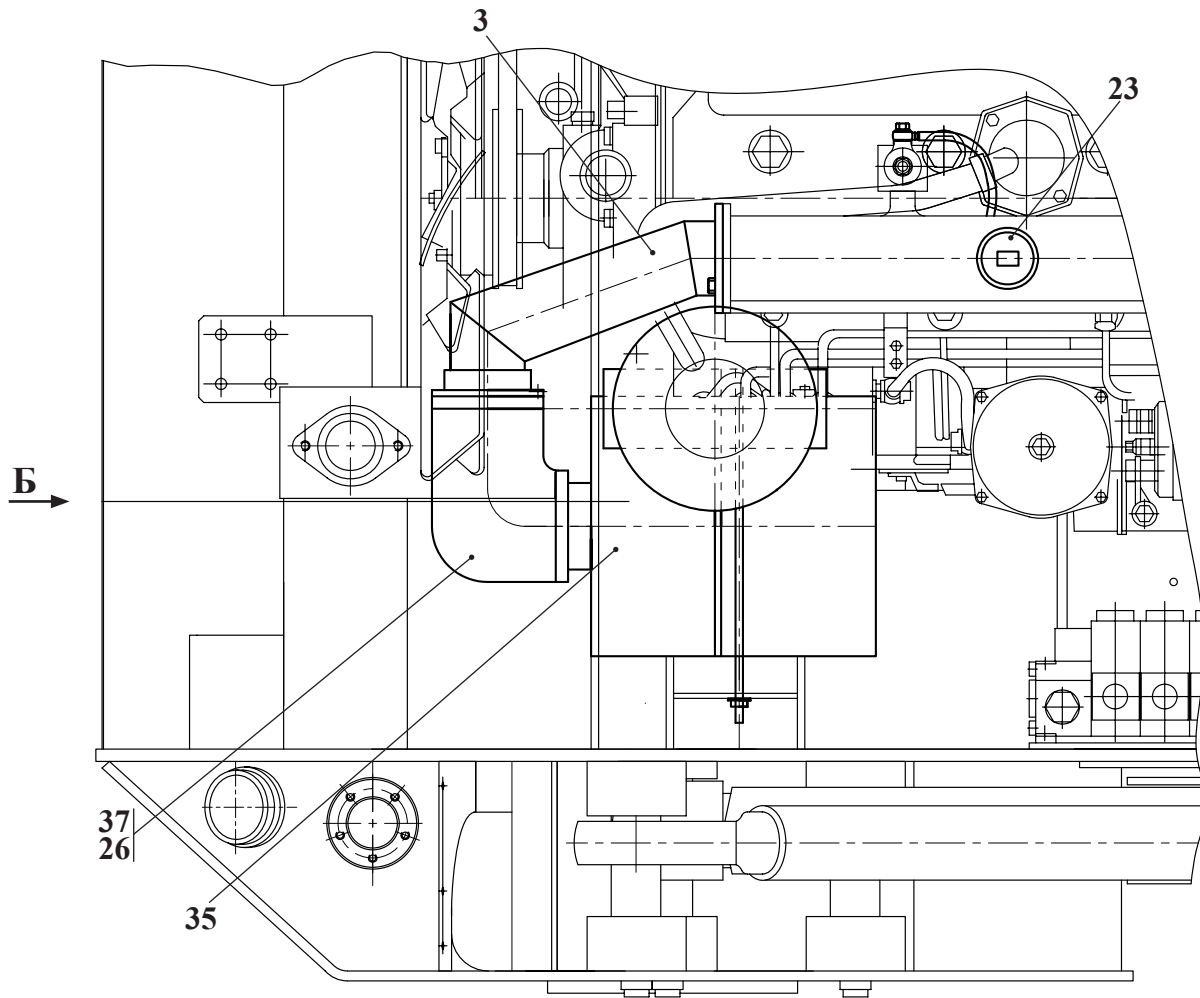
211.11.00.000-Б	Установка воздухоочистителя
